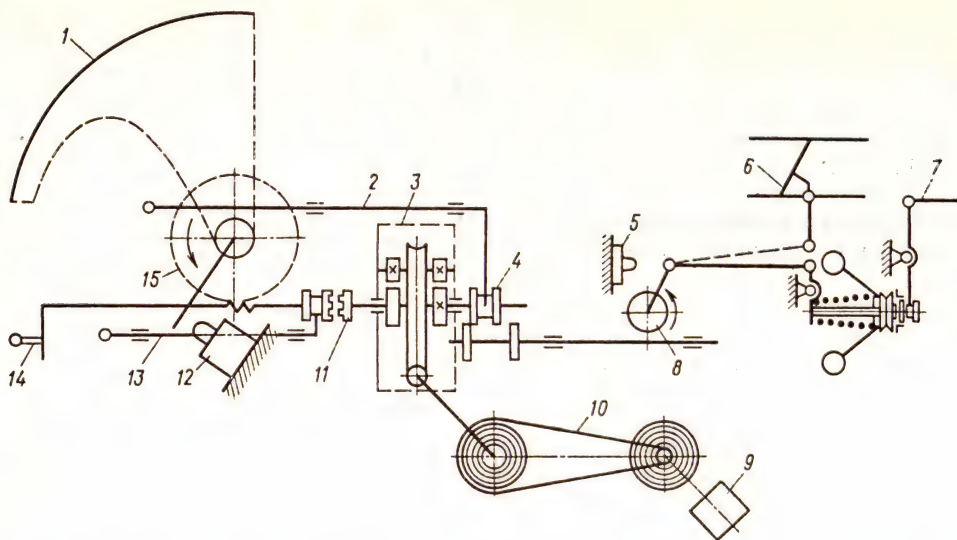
Кинематическая схема механизмов автоматического управления приработкой двигателей: 1 — электрод реостата; 2 — тяга переключения зубчатой передачи; 3 — планетарный редуктор; 4 — зубчатая передача; 5 и 12 — конечные выключатели; 6 — воздушная заслонка; 7 — тяга к рейке топливного насоса; 8 и 15 — червячные передачи; 9 — электродвигатель; 10 — ременная передача; 11 — кулачковая муфта; 13 — тяга включения кулачковой муфты; 14 — ручка реостата
